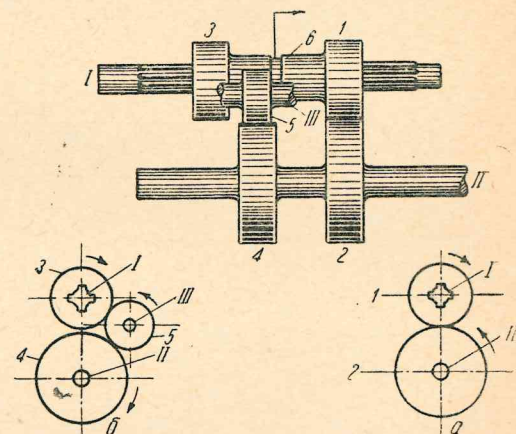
а. Схема реверсивной муфты с цилиндрическими колесами
